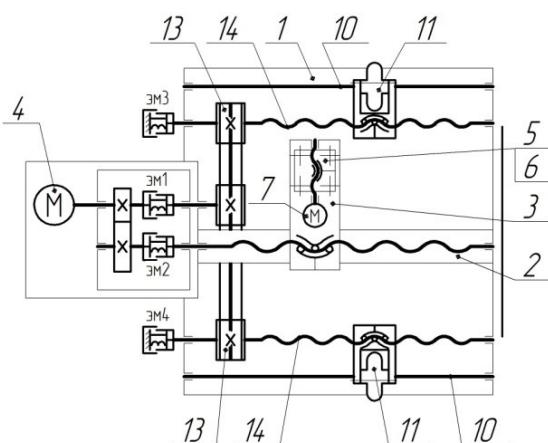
Кинематическая схема станка для обработки поверхностей крупногабаритных деталей-тел вращения
